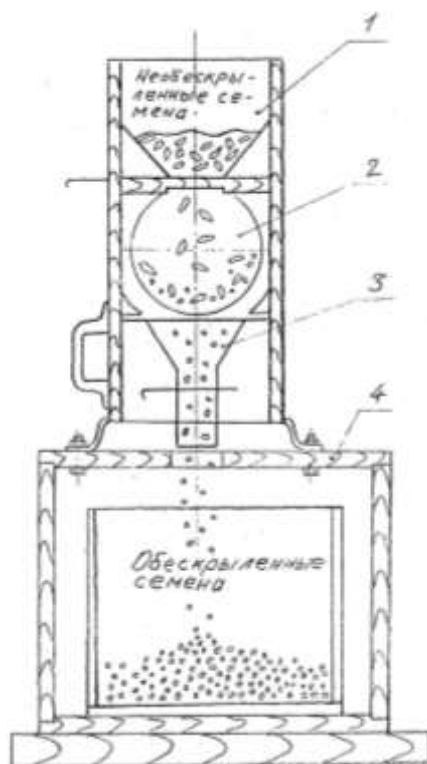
Обескрыливатель ВНИИЛХа конструкции Суровцева П.А.
